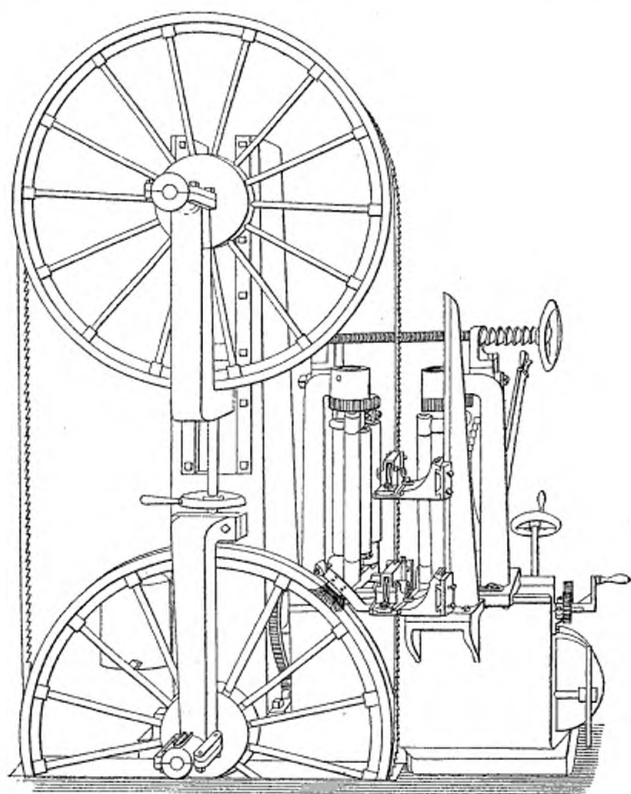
Machine à scier à refendre, montrant le support extérieur des poulies.
